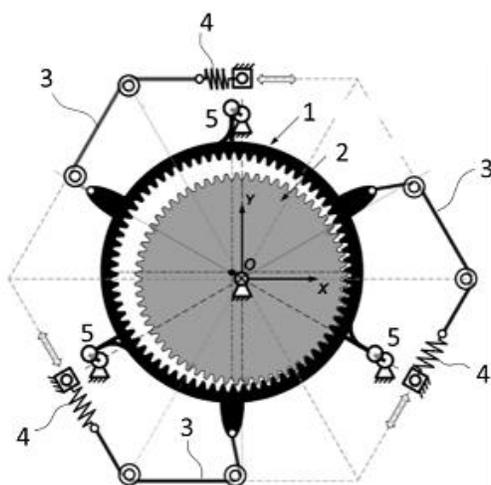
Шаговый двигатель (1 - коронная шестерня или эпицикл, 2 - центральная шестерня, 3 - проволоки из сплава с памятью формы, 4 – пружины, 5 - коленчатые валы).
